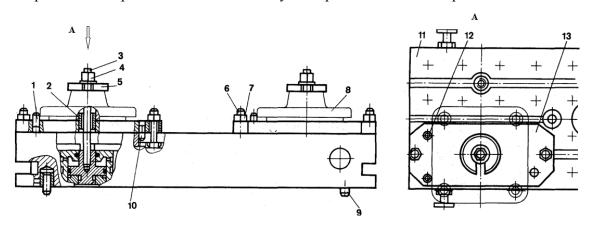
Приспособление двухместное для установки фланца: 1, 9, 12 — пальцы установочные, цилиндрические; 2 — втулка; 3 — шпилька; 4, 7 — гайки; 5 — шайба быстросъемная; 6 — болт станочный; 8 — заготовка; 10 — палец срезанный; 11 — плита; 13 — планка
